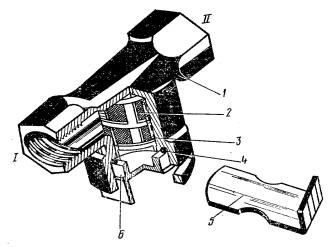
Фильтр магистральный: 1- корпус; 2- элемент фильтрующий; 3- пружина; 4- кольцо уплотнительное; 5- пластина; 6- крышка
